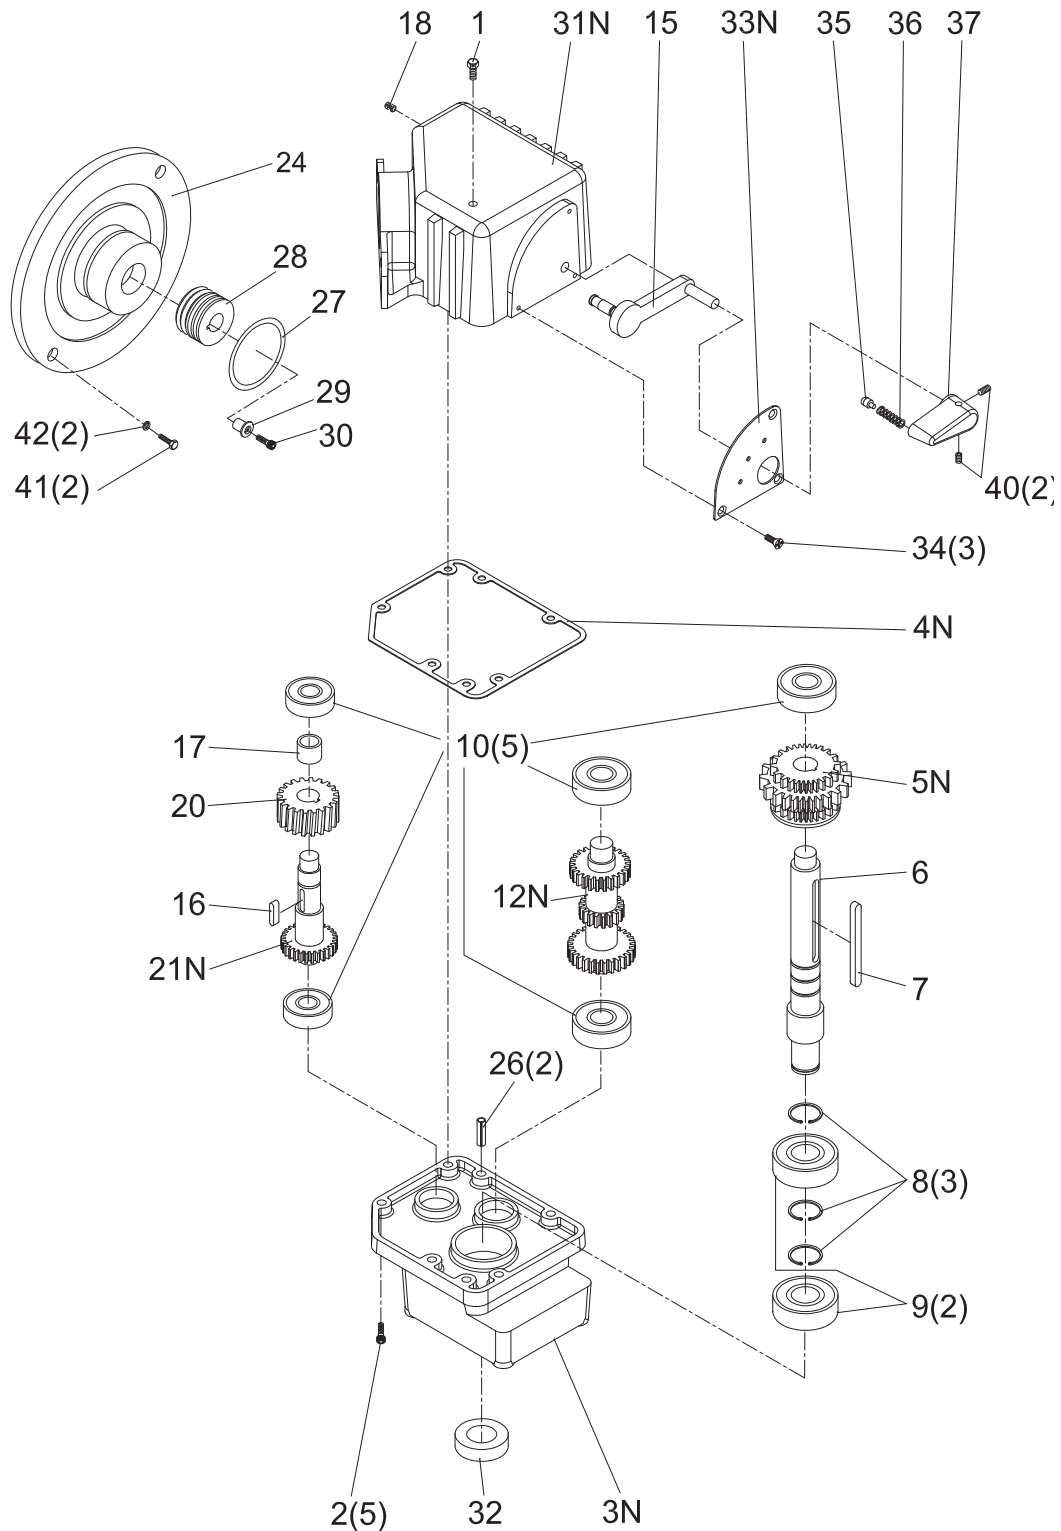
Explosionszeichnung Getriebe - Equipo de dibujo de explosión: 712 quinta generación
